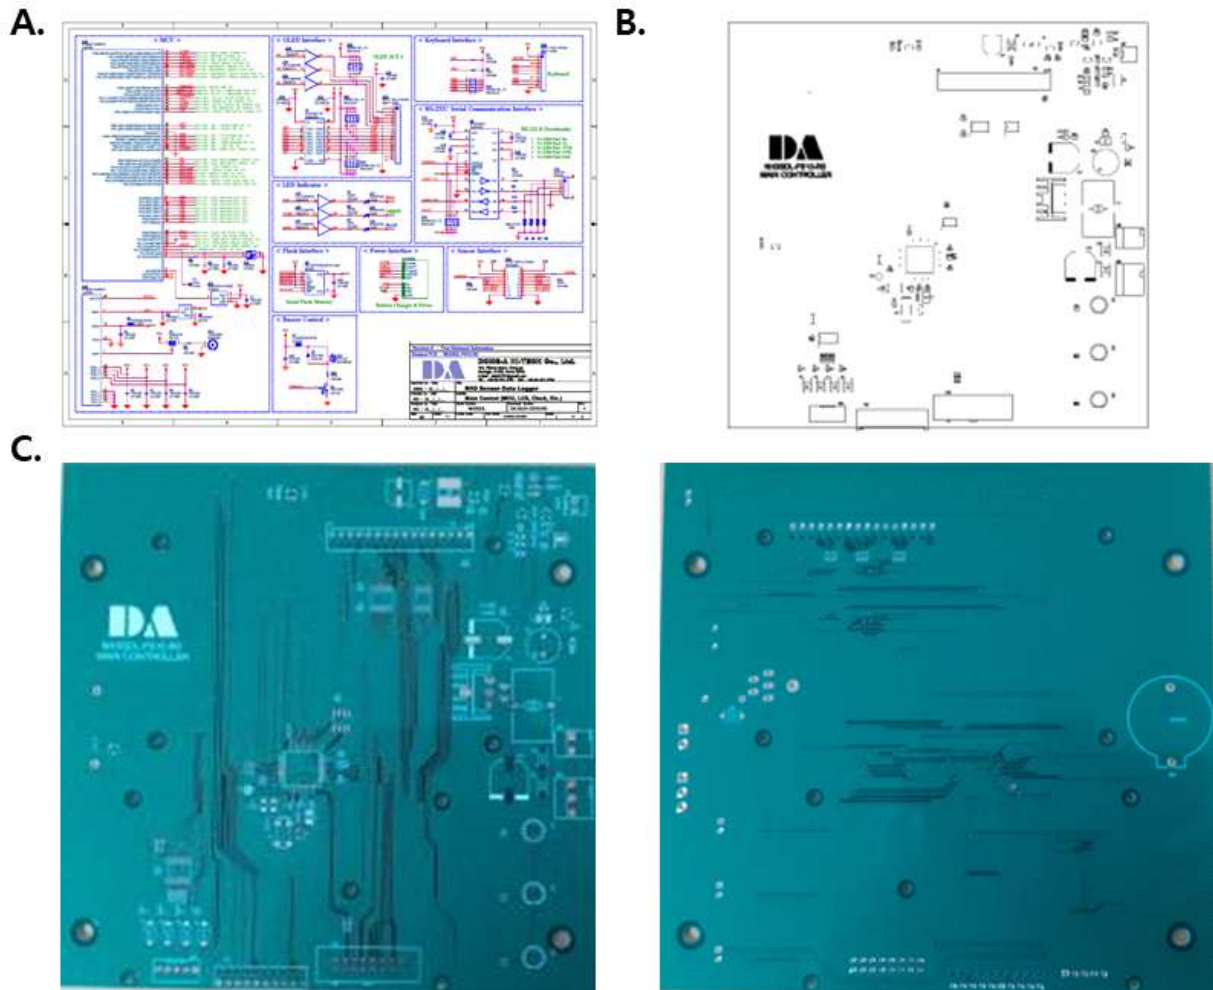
메인컨트롤 파트의 PCB. (A) 메인 컨트롤파트 회로도, (B) 메인 컨트롤파트 거버파일, (C) 메인 컨트롤파트 PCB
